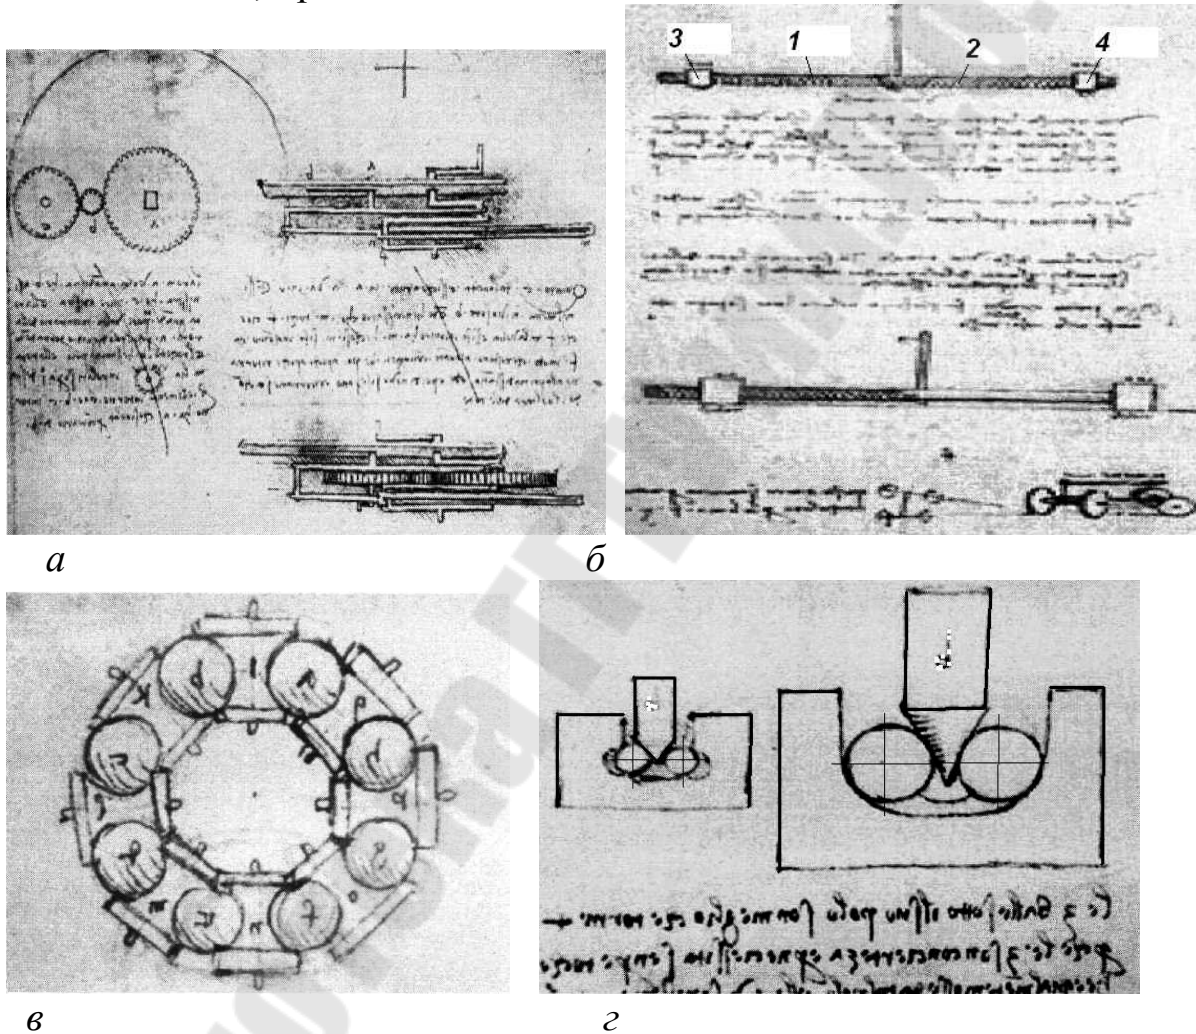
Рисунки Леонардо да Винчи механизмов: планетарного зубчатого (а), винтового реверса (б) (1, 2 – винт с разнонаправленной резьбой, 3, 4 – гайки); подшипников (радиального и радиально-упорных) (в,г).
